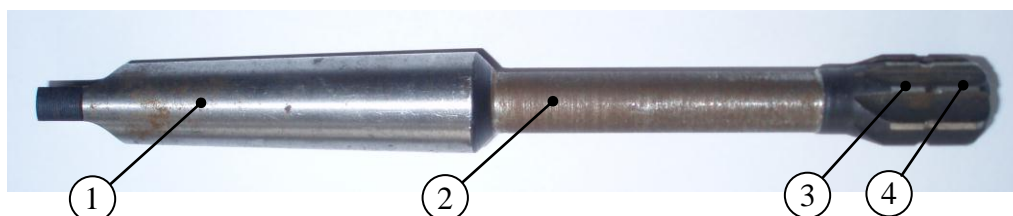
Двухступенчатая развертка для обработки точных отверстий [5]:
